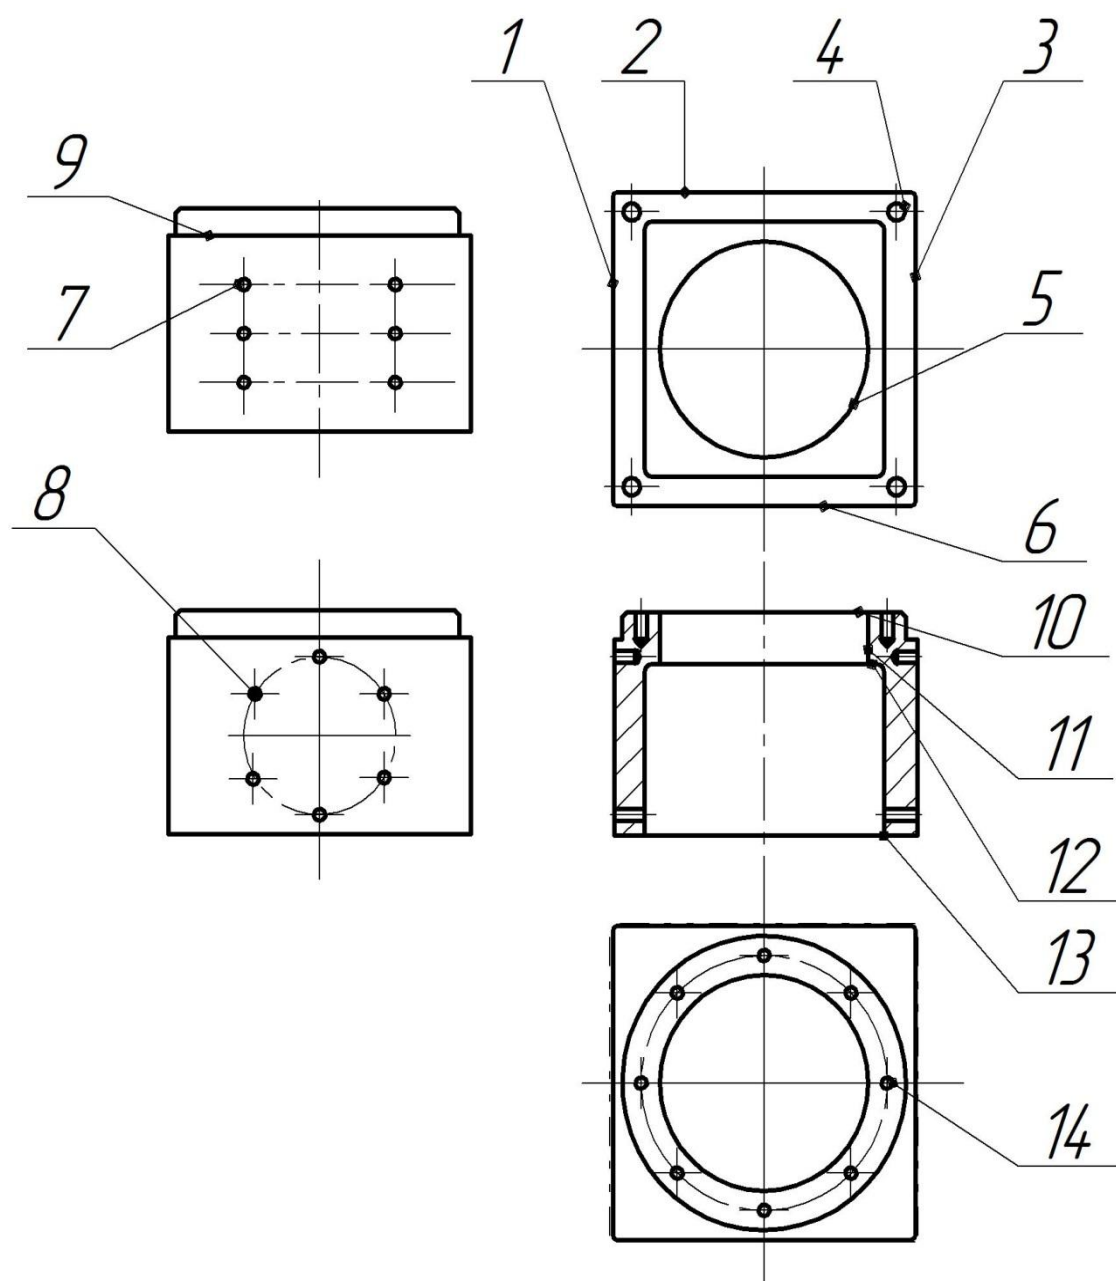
Деталь - «Корпус приспособления», общий вид
